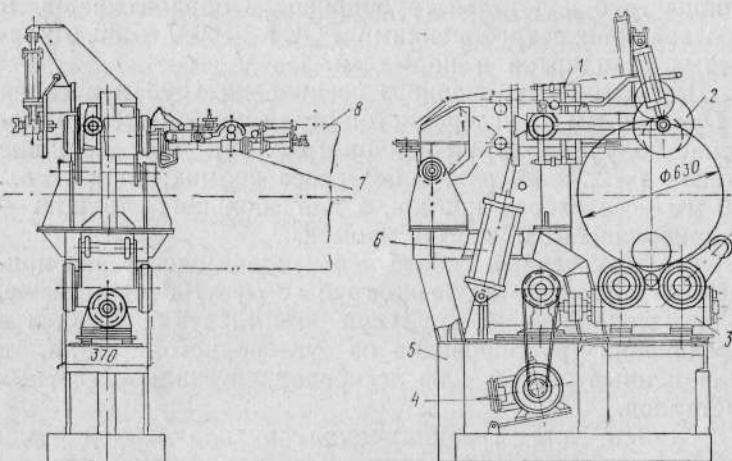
Установка УРТ-630М для газопламенной и плазменной резки труб
